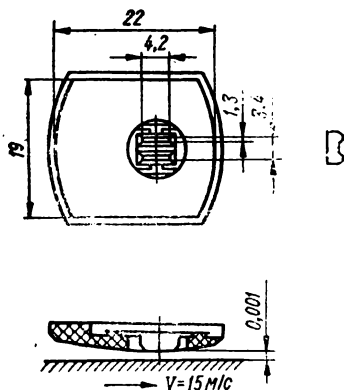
Стабилизирующая опора и магнитная головка устройства двойного подвеса
